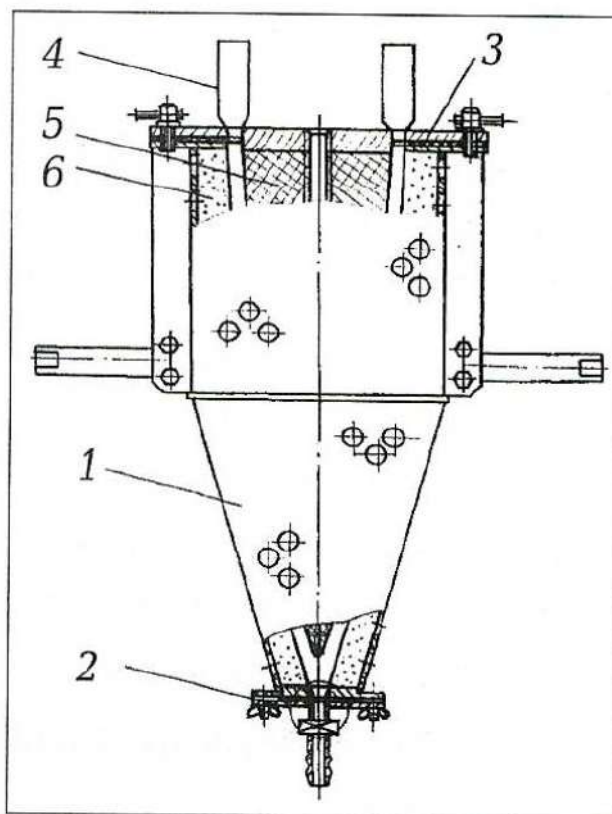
Принципиальная схема формового комплекта для литья керамических заготовок из водных шликеров [40]: 1 – перфорированный металл, 2 – нижний фланец со штуцером для заполнения полости формы шликером, 3 – опорный фланец, 4 – подпиточные емкости, 5 – сердечник, 6 – активная поверхность пористой формы.
